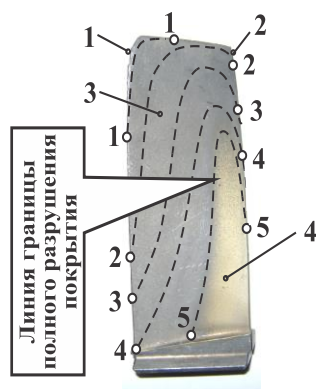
Схема неравномерного эрозионного разрушения (неравномерность 1-го ранга) пера лопатки компрессора ГТД
